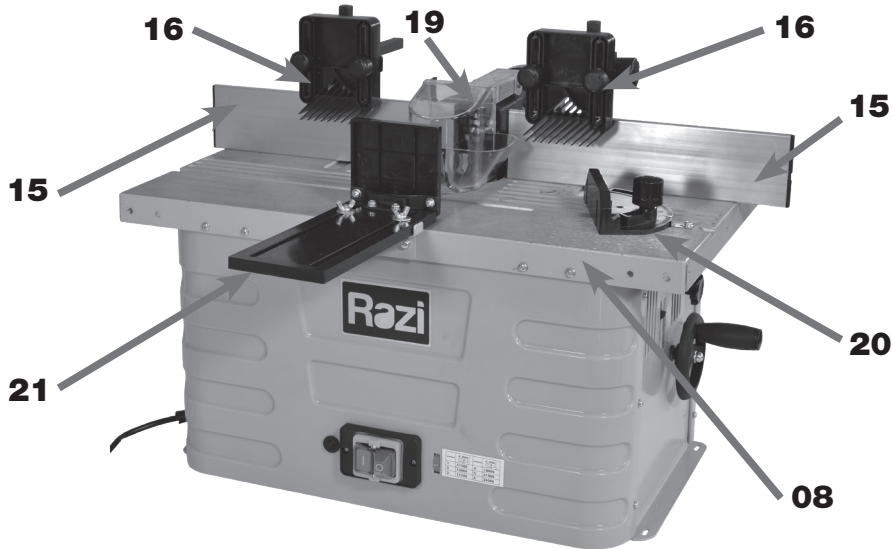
Conjunto da Guia e Barra Pressão Frontal
